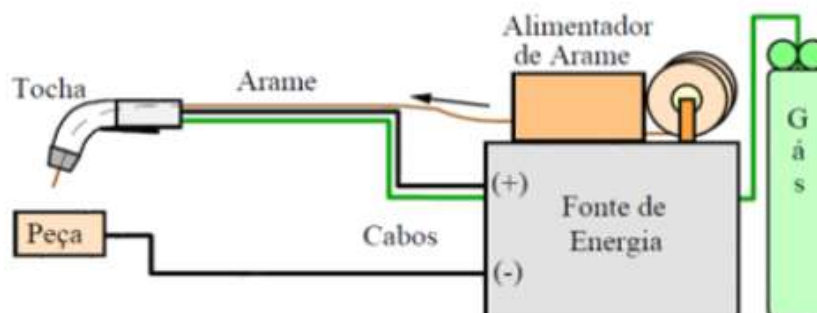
Esquema do processo de soldagem MIG/MAG (Rodrigues, 2011).
